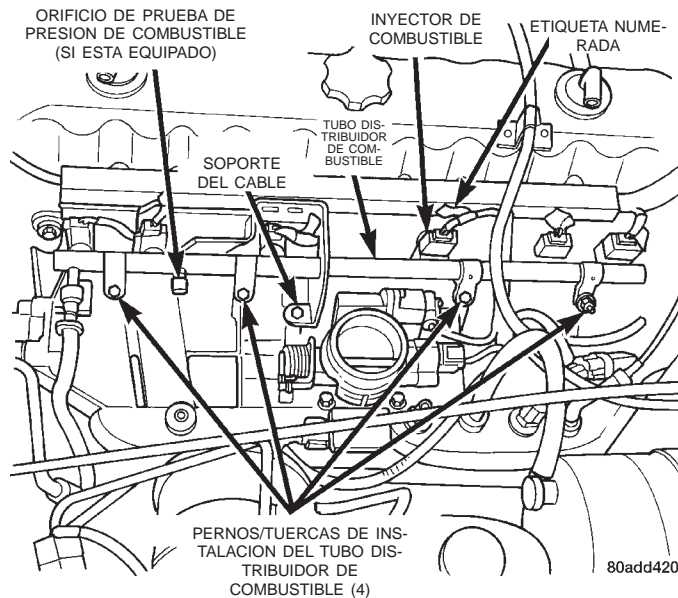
Montaje del tubo distribuidor de combustible—Motor 4.0L
